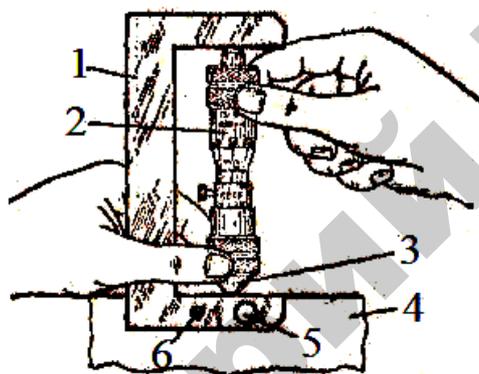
Проверка нулевой установки микрометрического нутромера:
